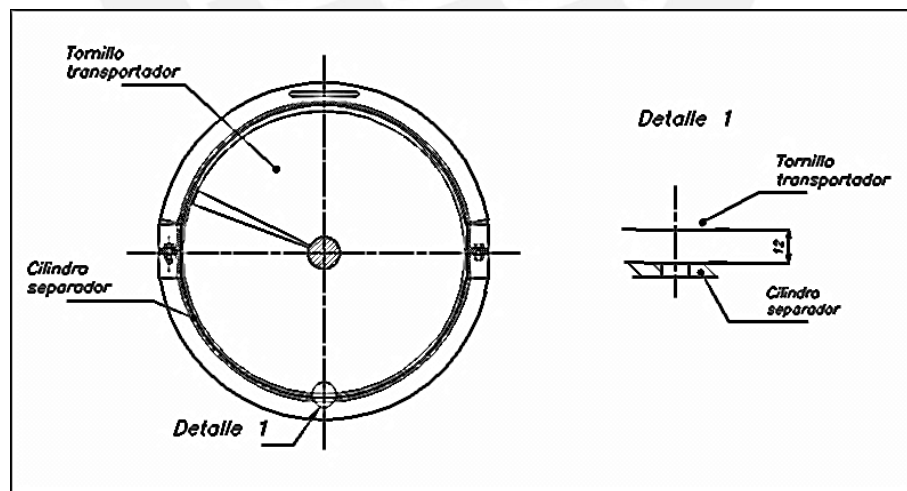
Ensamble transportador de tornillo – cilindro separador
